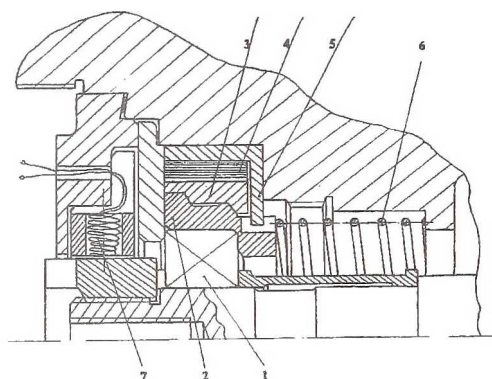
Общий вид узла с исследуемой упругодемпферной опорой с многослойного типа: 1- подшипник; 2 - втулка; 3 втулка, разрезанная на сегменты; 4 - демпфер; 5 - корпус демпфера; 6 - пружина; 7 - датчики перемещений.
